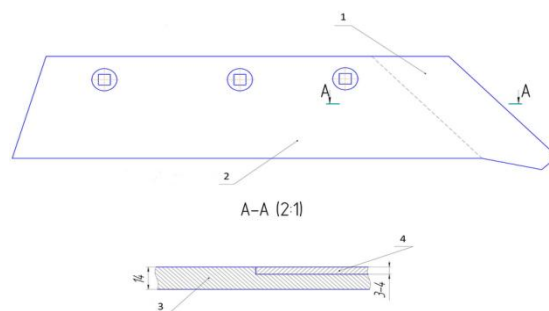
Конструкция предлагаемого лемеха: 1- долотообразная часть; 2- основа; 3- металлическое основание; 4- верхний абразивностойкий слой
